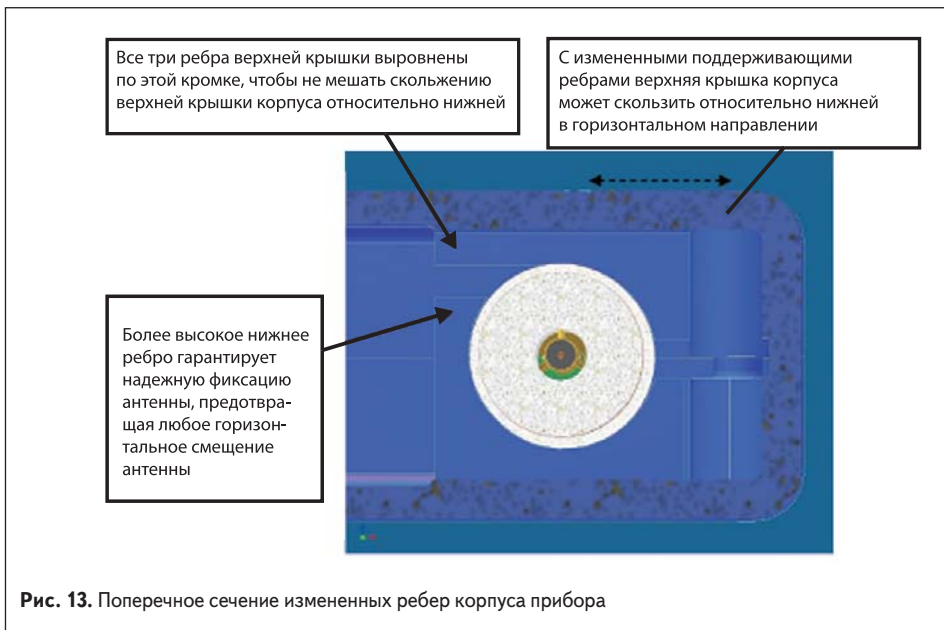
Поперечное сечение измененных ребер корпуса прибора
